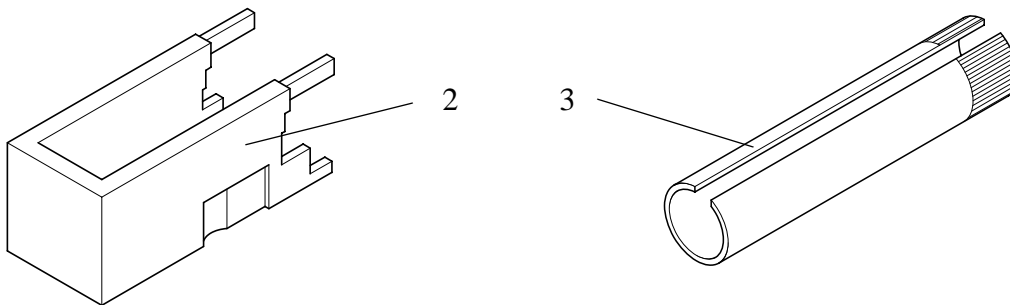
Demontage-Werkzeug (2) und Montageschlüssel (3)
